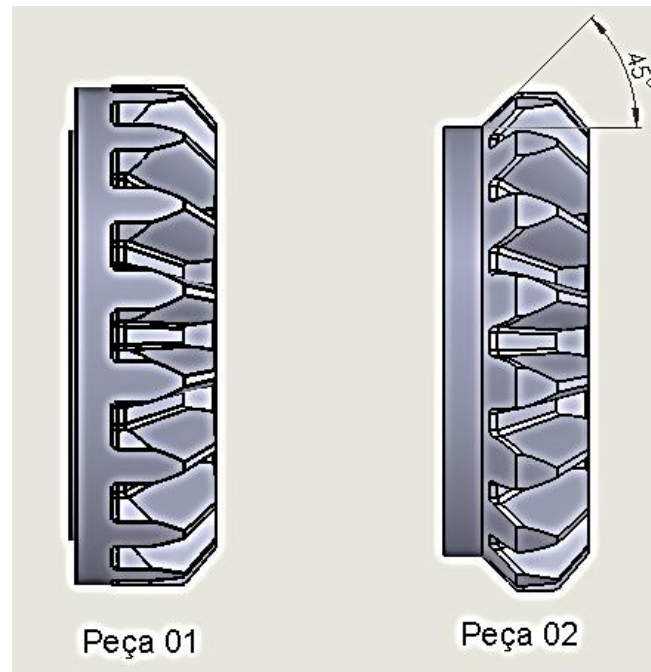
(peça 01) Engrenagem sinterizada; (peça 02) engrenagem usinada.
